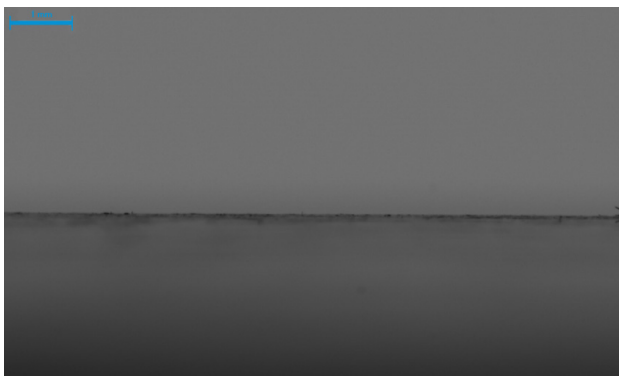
Поверхность шлифованной пластины из нержавеющей стали марки «AISI 304»
